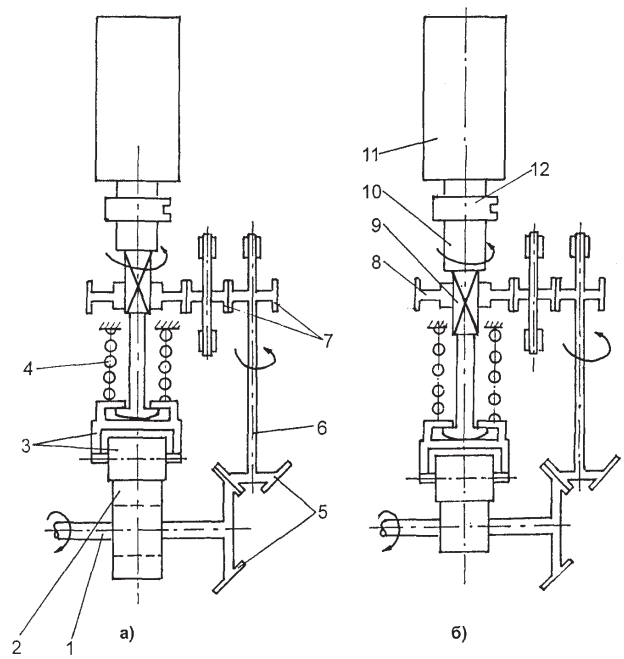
Схема привода плунжера с внешним цилиндрическим кулачковым профилем:
